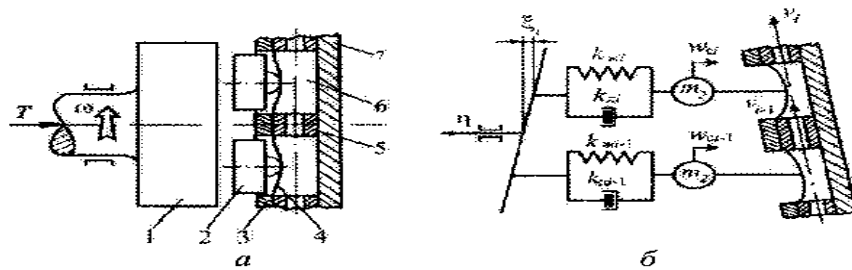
Принципова (а) та розрахункова (б) схеми УПК з ГВП: 1- гребінь; 2 - подушка; 3- сепаратор; 4- ТПК; 5- ребро жорсткості; 6- кільцева камера; 7- корпус
